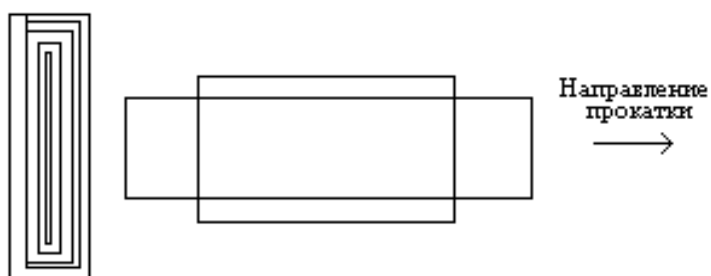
Образец с обкладкой: 1-алюминиевая пластинка; 2-свинцовая обкладка
